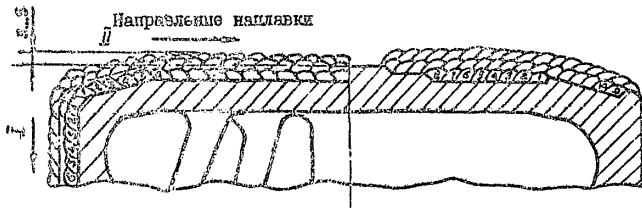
Схемы дуговой наплавки дна и наружной цилиндрической поверхности головки поршня
